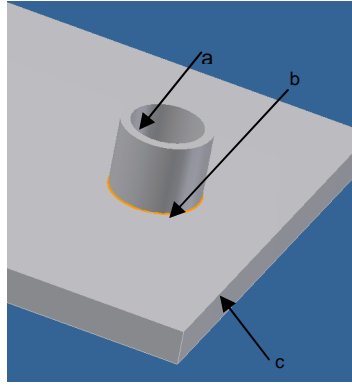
Soldadura chimenea con techo de cámara de secado.
